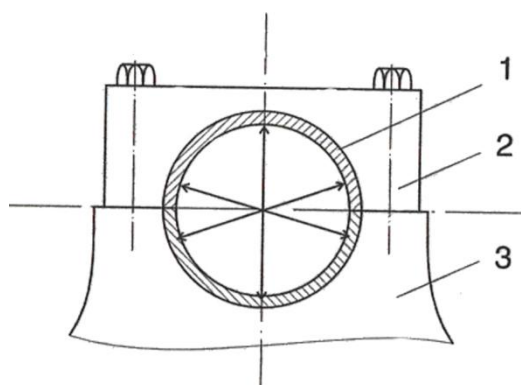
Схема проверки внутреннего диаметра подшипника коленчатого вала: 1 – вкладыш, 2 – крышка, 3 – основание. Стрелками указаны плоскости измерения внутреннего диаметра.
